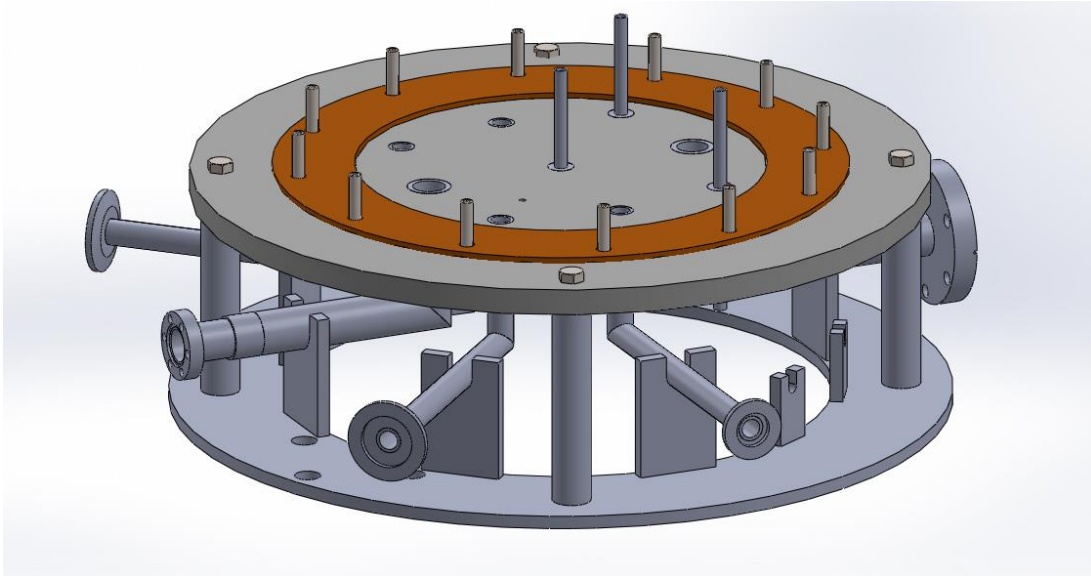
Vista dimétrica del empaque plano colocado en la base de la Cámara Inerte.
